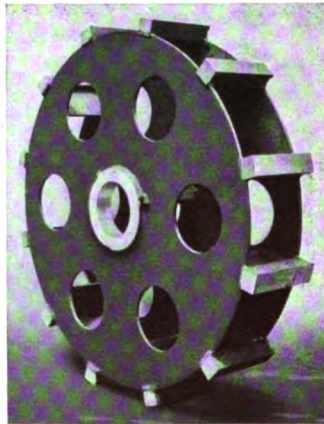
Geschweißtes Läuferferrad eines Asynchronmotors.
